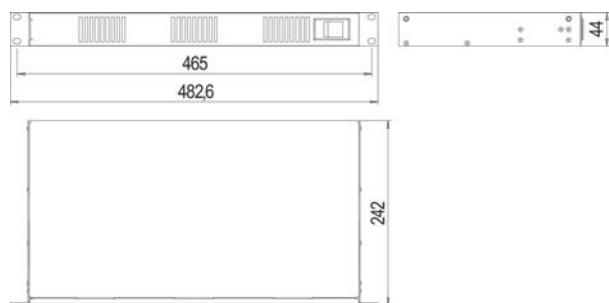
Габаритный чертеж ЩРЗ-7
